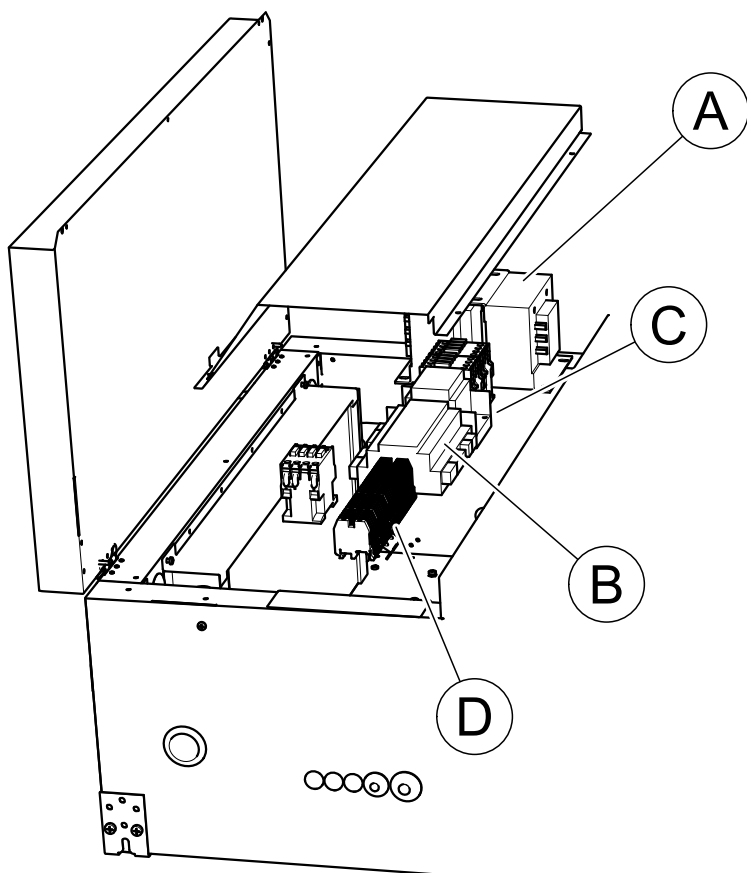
Соединительная коробка ТА 1400-4500 HW
